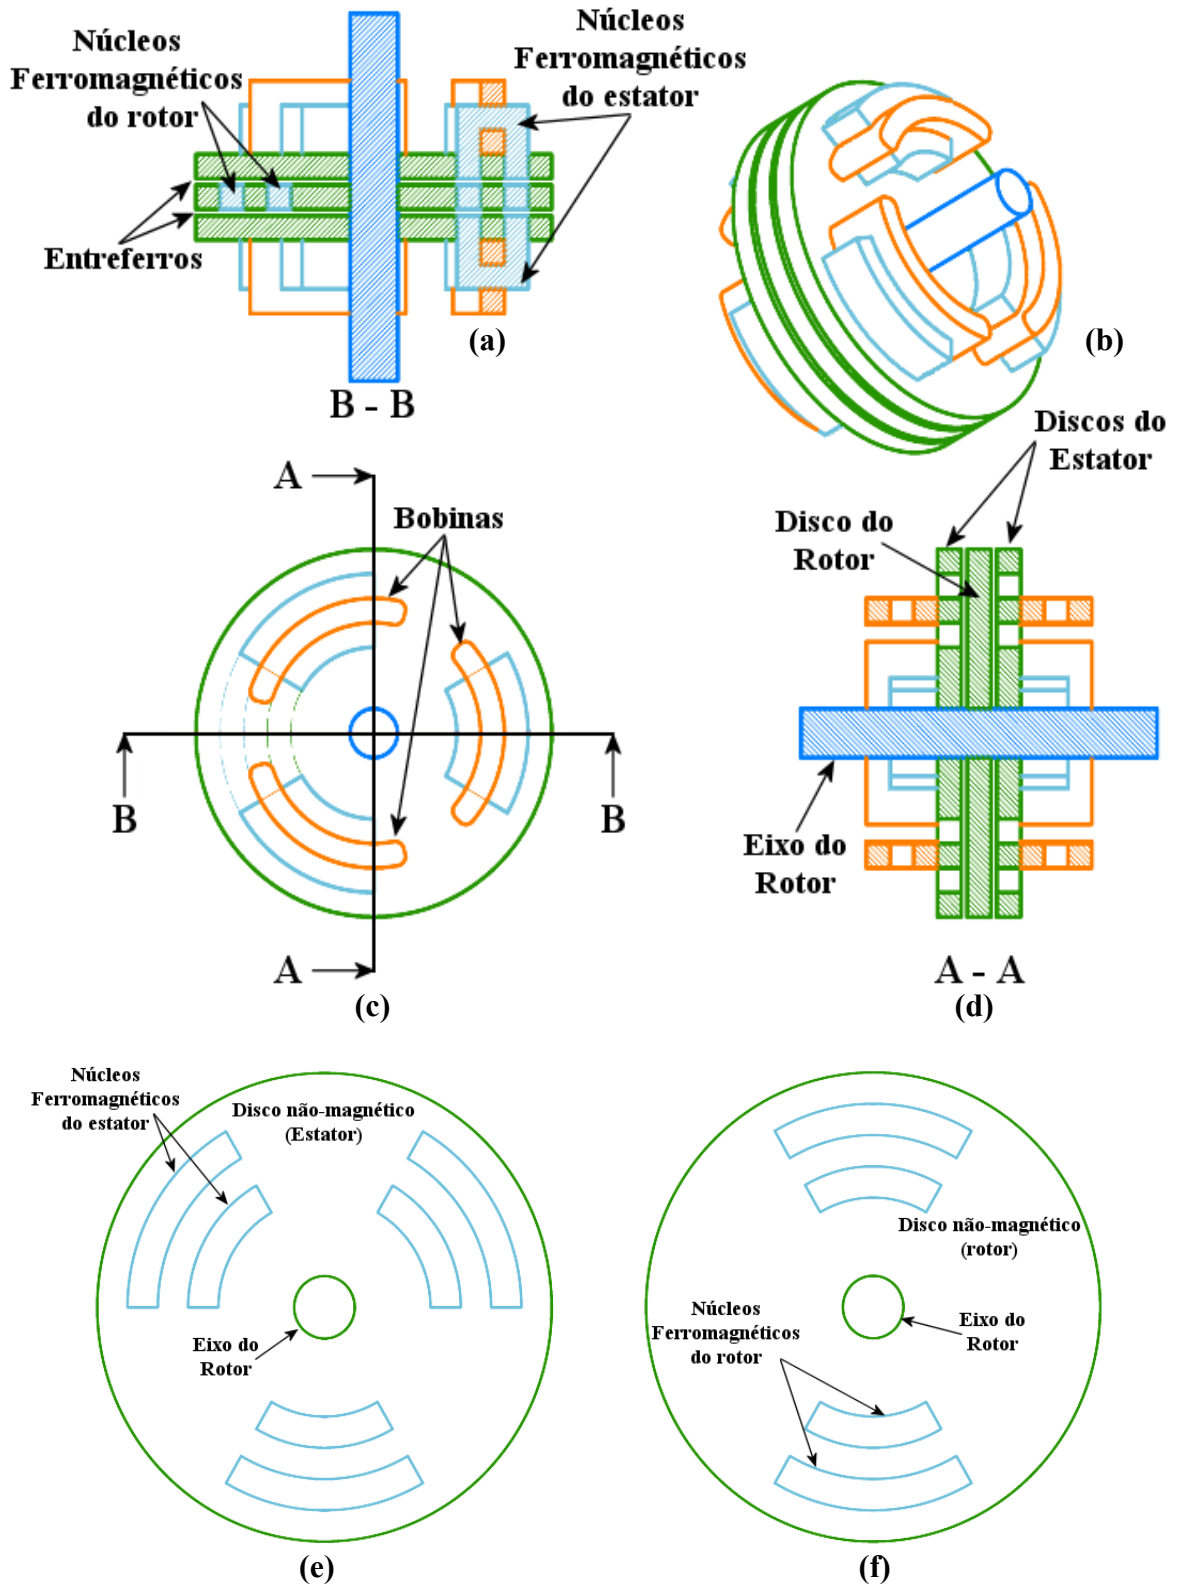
Motor rotativo de relutância chaveado de fluxo axial: (a) corte B-B, (b) vista em perspectiva, (c) vista frontal, (d) corte A-A, (e) vista frontal do disco não-magnético e dos pólos do estator e (f) vista frontal do disco não-magnético e dos pólos do rotor (KRISHNAN, 2001a, adaptado)
